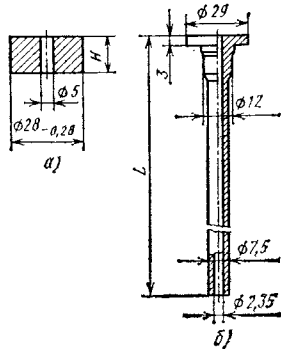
Заготовка (а) и поковка (б) венглия шины грузового автомобиля
